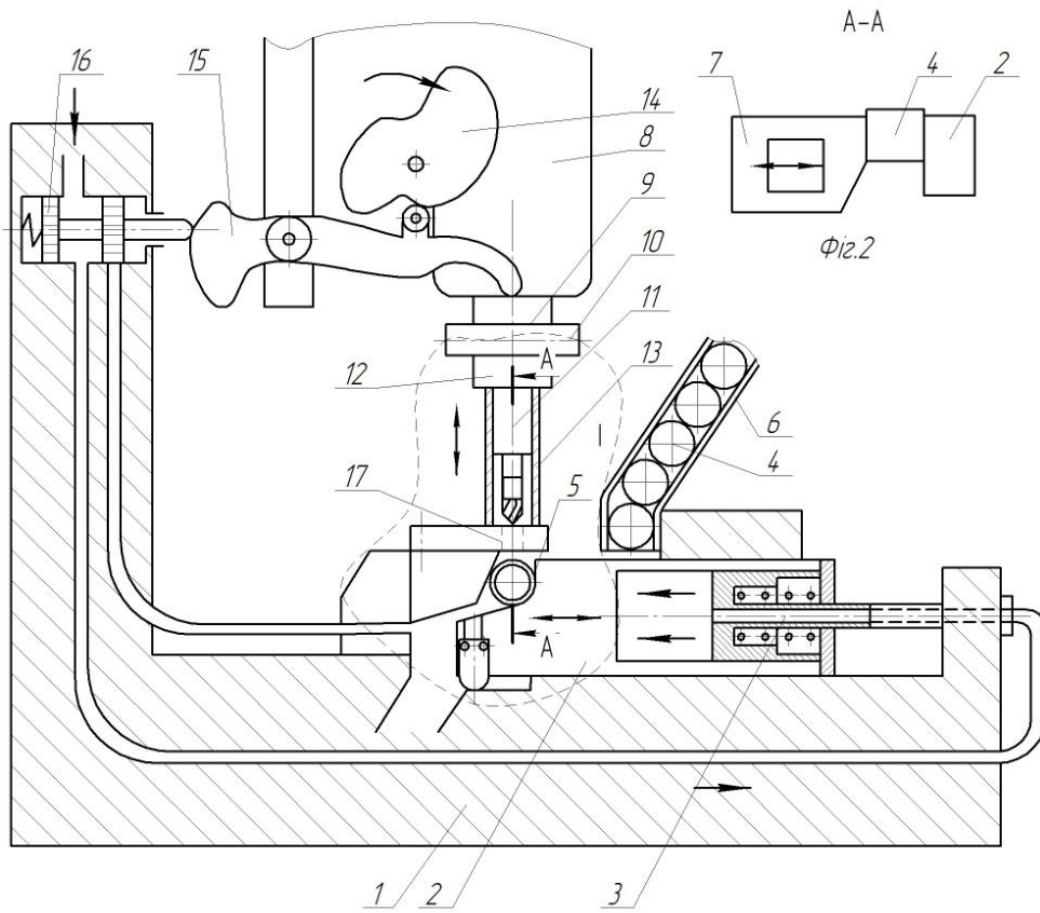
Пневматичний автоматизований пристрій для свердління і нарізання різи в трубчастих заготовках
